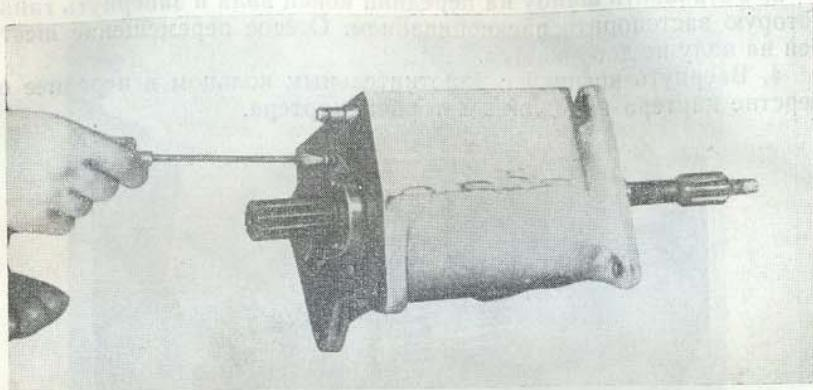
Крепление вторичного вала коробки передач автомобиля УАЗ-452
